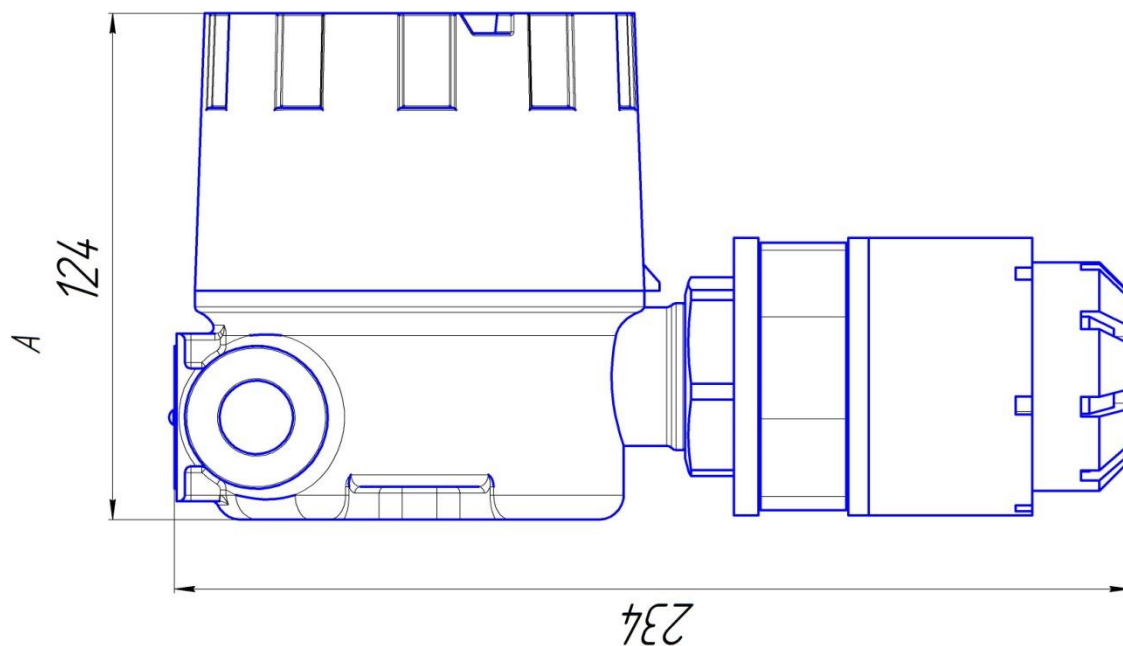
Габаритный чертеж ДГС ЭРИС-230
